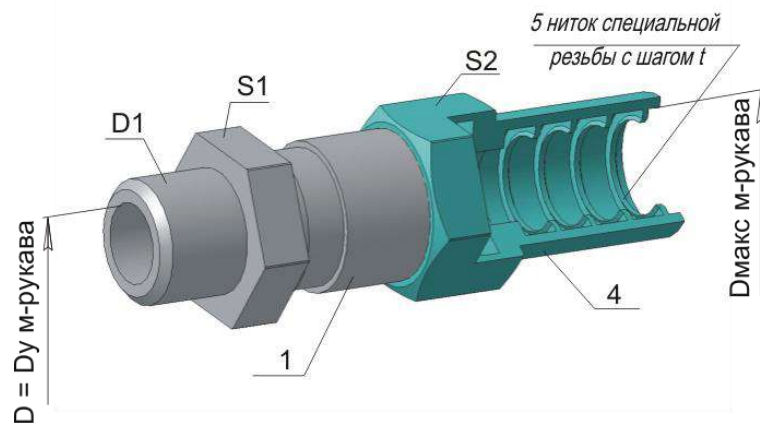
Конструкция кабельного ввода для монтажа кабеля в металлорукаве
